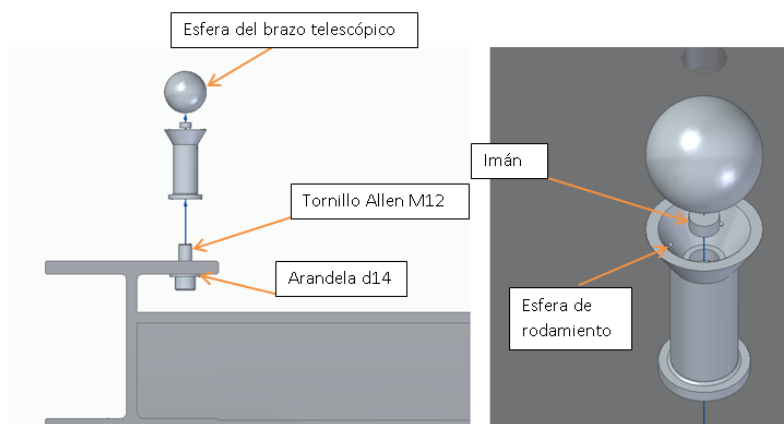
Montaje del "utillaje nido bola" y la posición de sus componentes.
